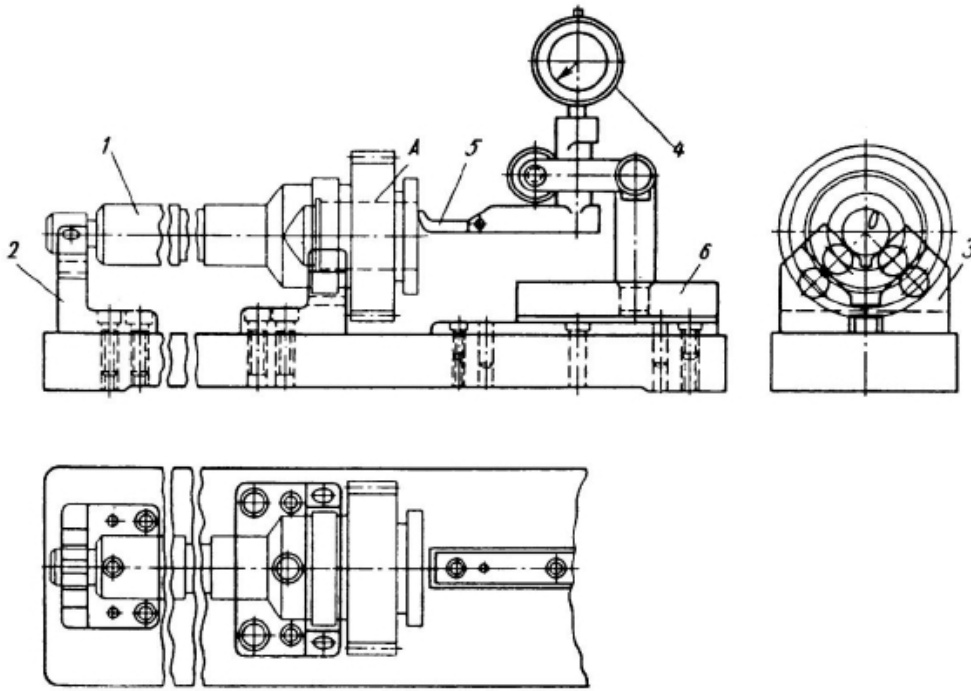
Контрольне пристосування для вимірювання биття: 1 – контрольована деталь; 2, 3 – роликові призми; 4 – індикатор; 5 – важільна передача; 6 – стійка
